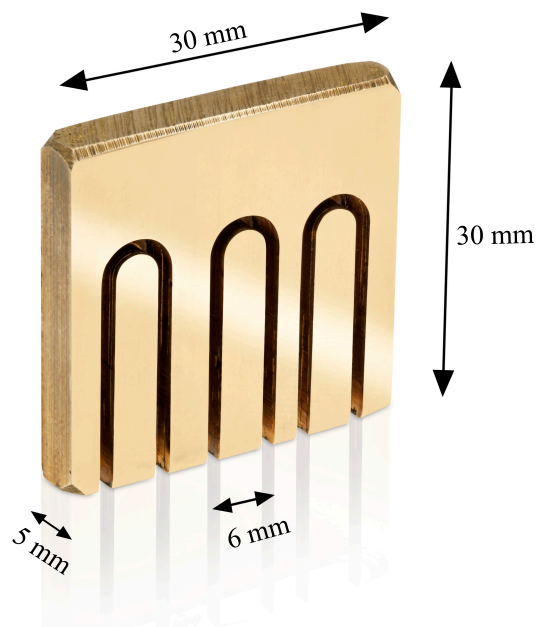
Messingblock mit gefräster U-Nut für die Drahtformgebung.
